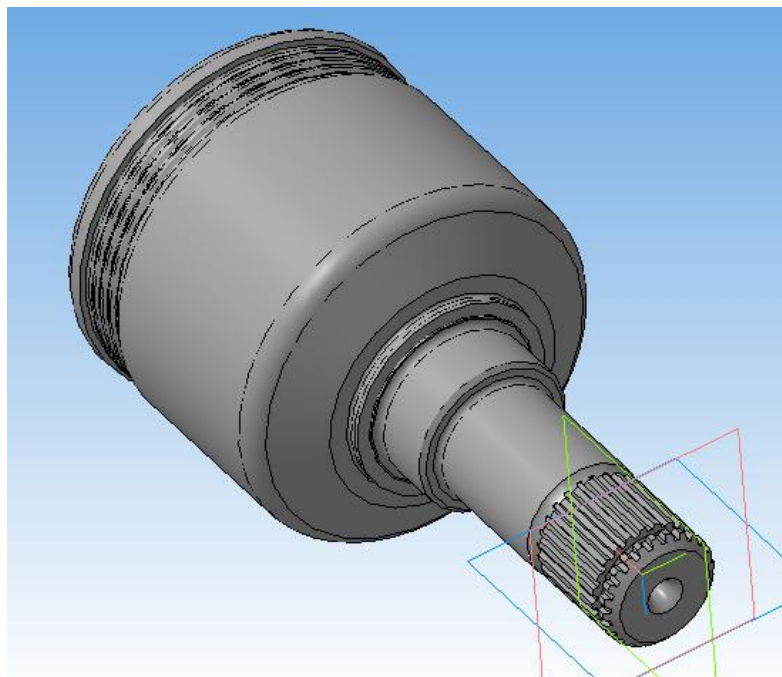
3D модель детали корпус внутреннего шарнира
